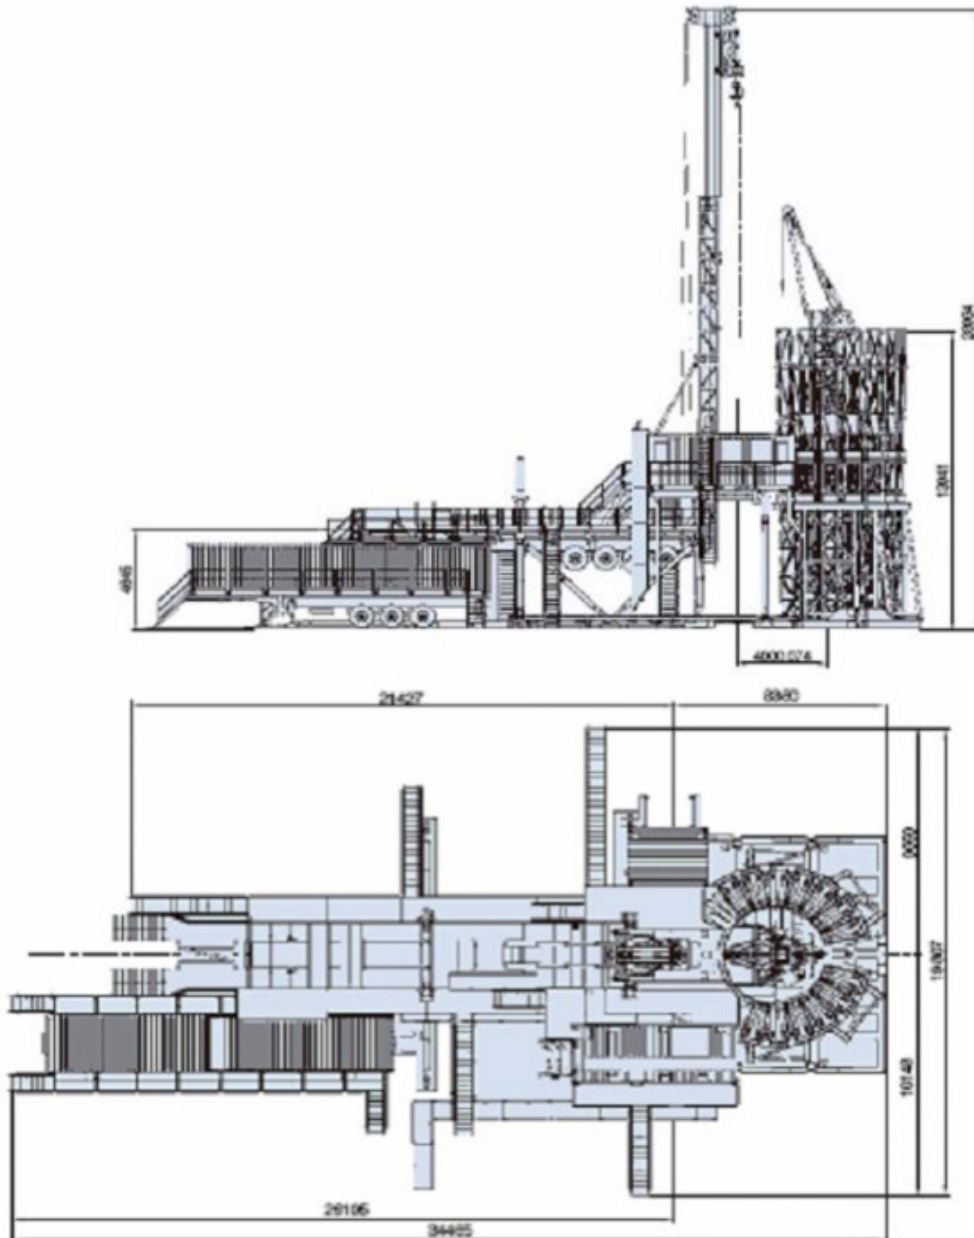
Planimetria dell'Impianto di Perforazione HH220
